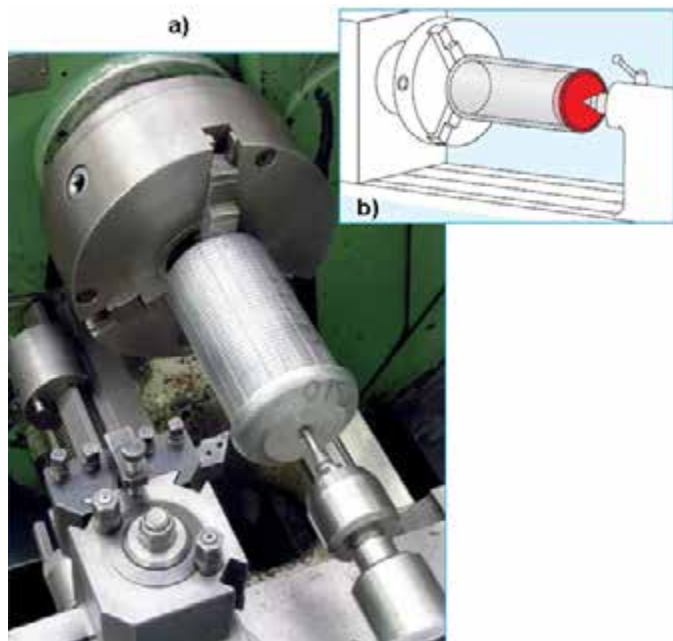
ro-44: Обработка заготовки гильзы цилиндра в требуемый размер производится на токарном станке; источник: MSI
